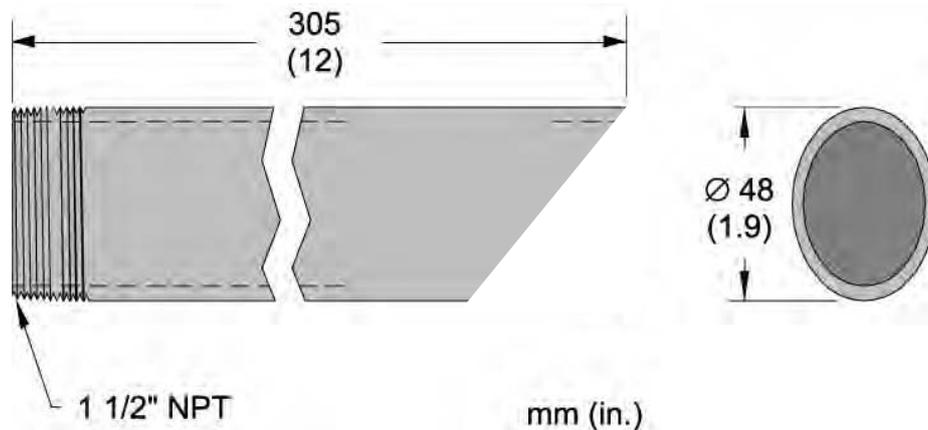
Tube de visée acier de 300 mm coupé à 45° (E-BEESIGHT)
